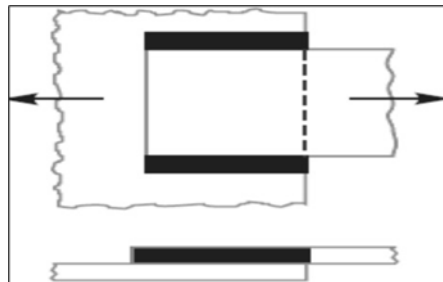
पॅरालेल फिलेट वेल्ड (Parallel Fillet Weld)
